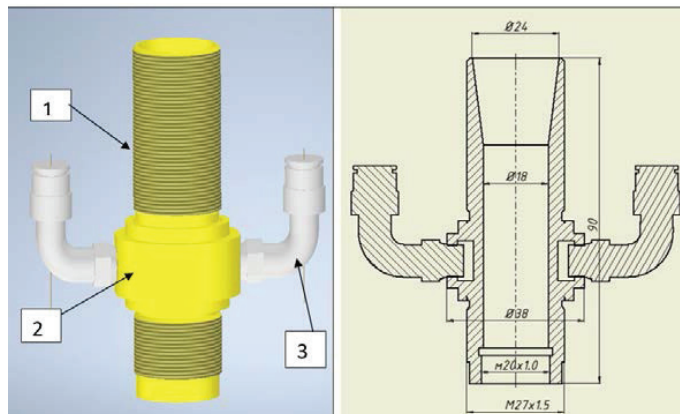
Модель (а) та ескізне креслення частини головки для лазерного наплавлення з системою водяного охолодження (б), де 1 – корпус для проходження лазерного випромінювання; 2 – корпус водяного охолоджувача; 3 – штуцер подачі охолоджуючої рідини
